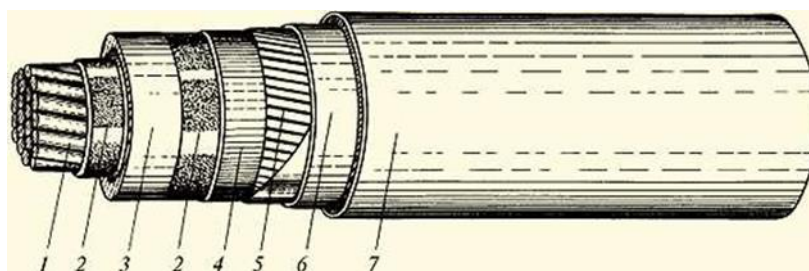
Конструкция кабеля на 10 кВ: 1 - ТПЖ; 2 - электропроводящие экструдированные экраны; 3 - изоляция; 4 - электропроводящие влагонабухающие ленты; 5 - экран из медных проволок; 6 - разделительная обмотка лентой; 7 – оболочка
